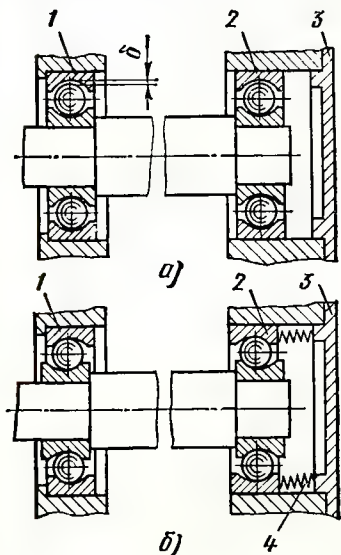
Положение колец и шариков без предварительного натяга (а) и с предварительным натягом (б)
